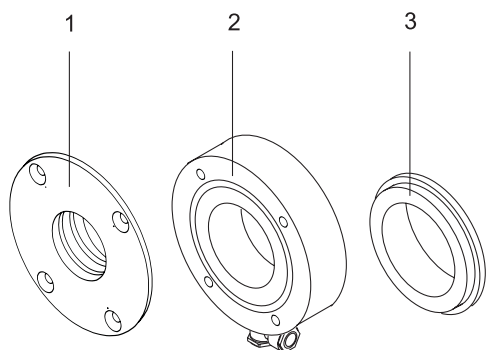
SPA FM 1/8 y compris support soudable SPA
